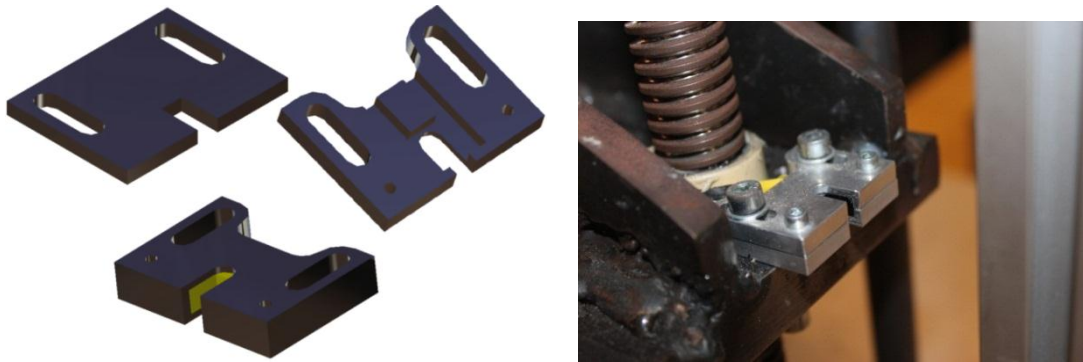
Esboço final da caixa de suporte para o sensor à esquerda e caixa de suporte do sensor montado na máquina à direita.
